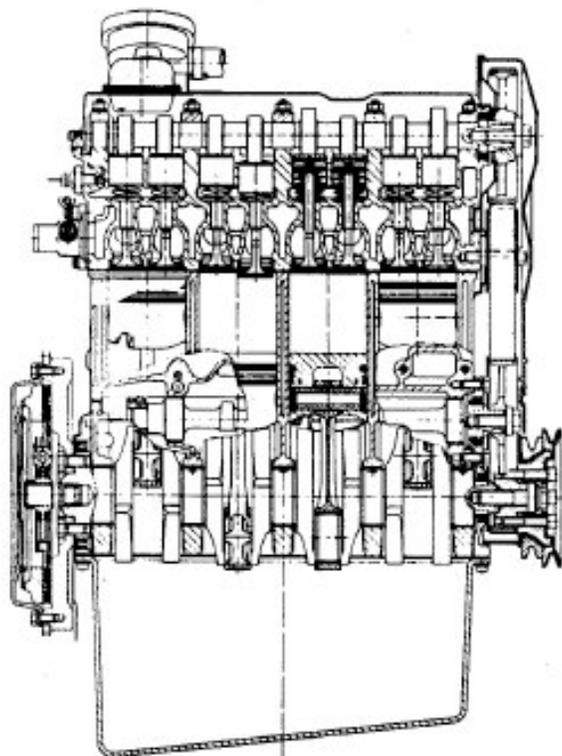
Längs- und Querschnitt des Vierzylinder-Turbodieselmotors von VW
